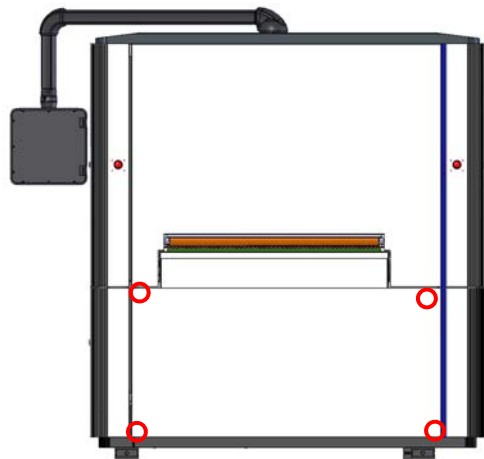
Abdeckblech Maschinenauslaufseite entfernen
